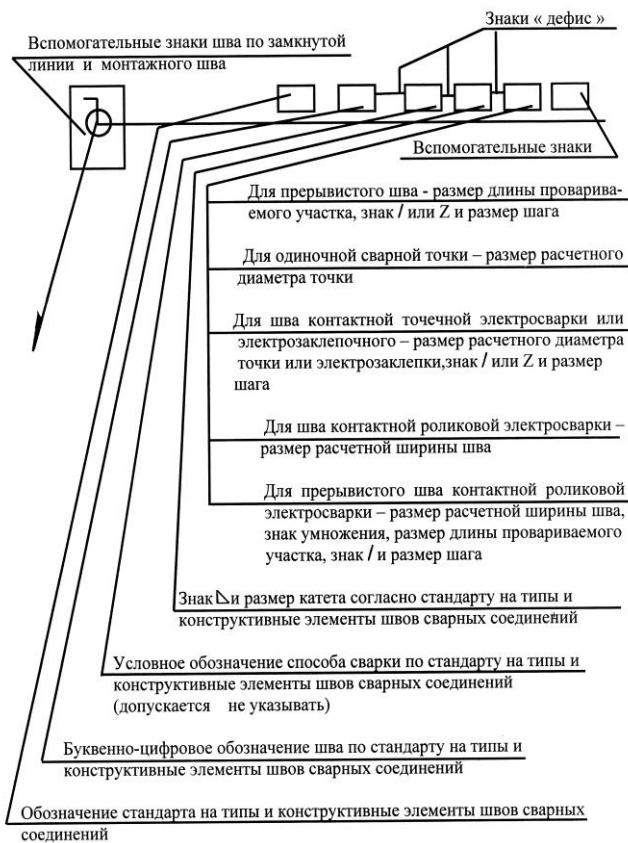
Структура условного обозначения сварного шва на чертежах (ГОСТ 2.312-72\*)
